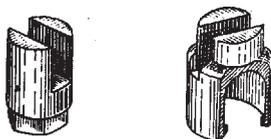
Предохранительные насадки на головки краскораспылителя
